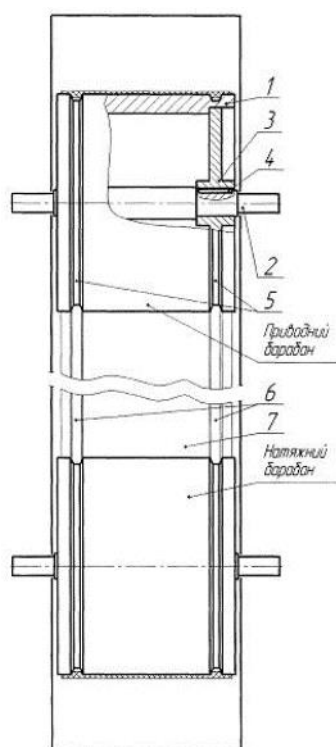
Деклараційний патент UA 49254. Вертикальний ківшевий стрічковий елеватор
